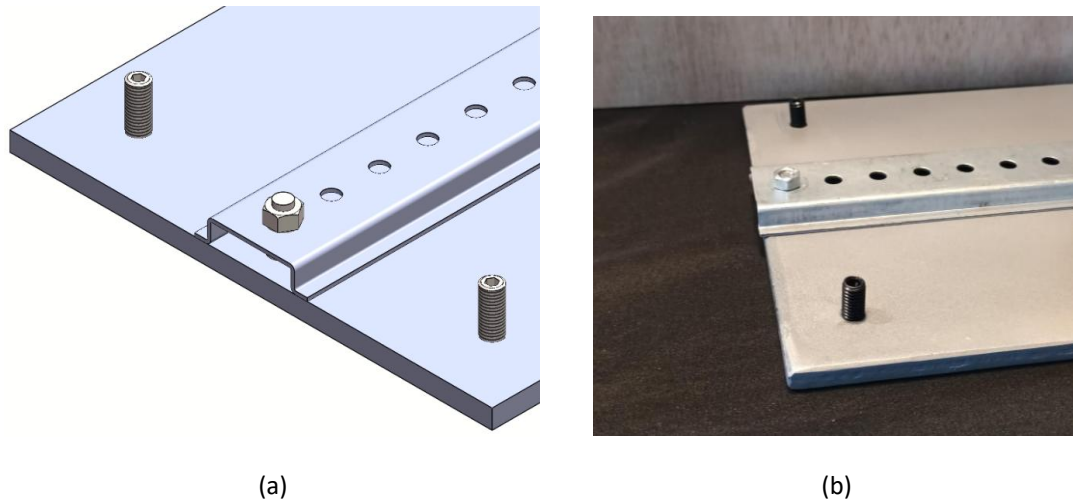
Base da balança. (a) Modelação em CAD. (b) Construção.
